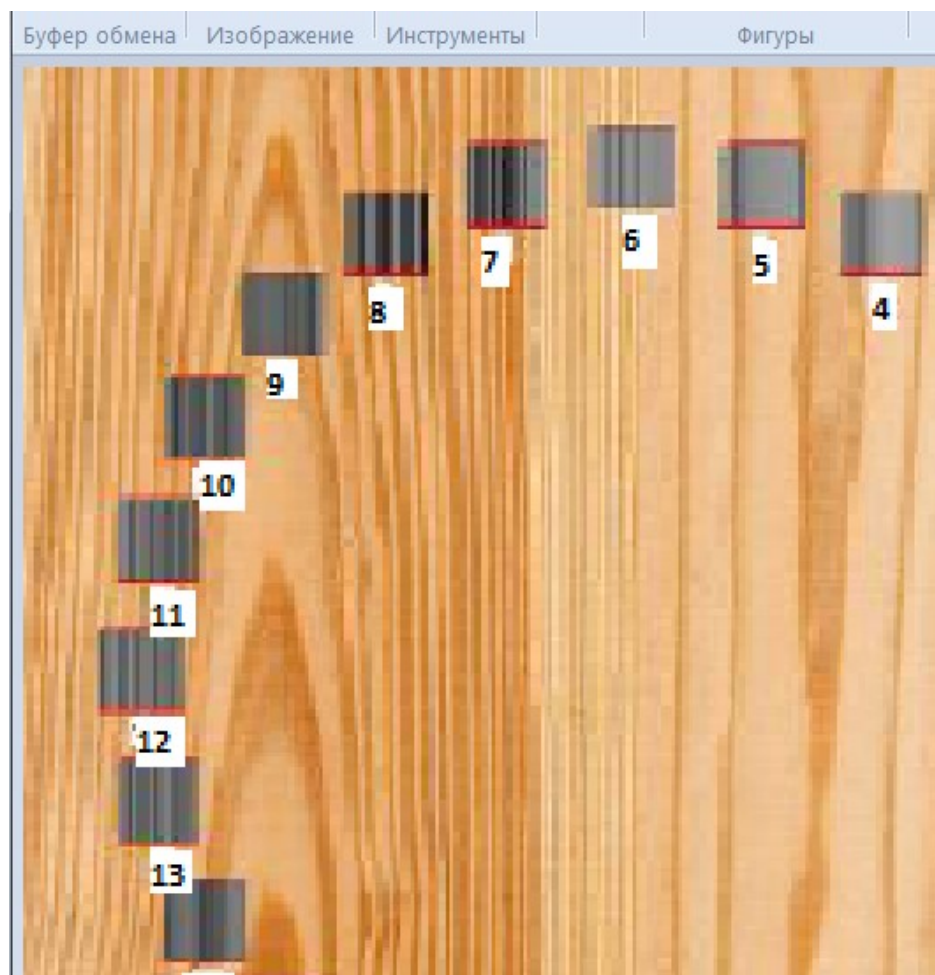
Розподіл заготовки на локальні зони для фрезерування по колу
